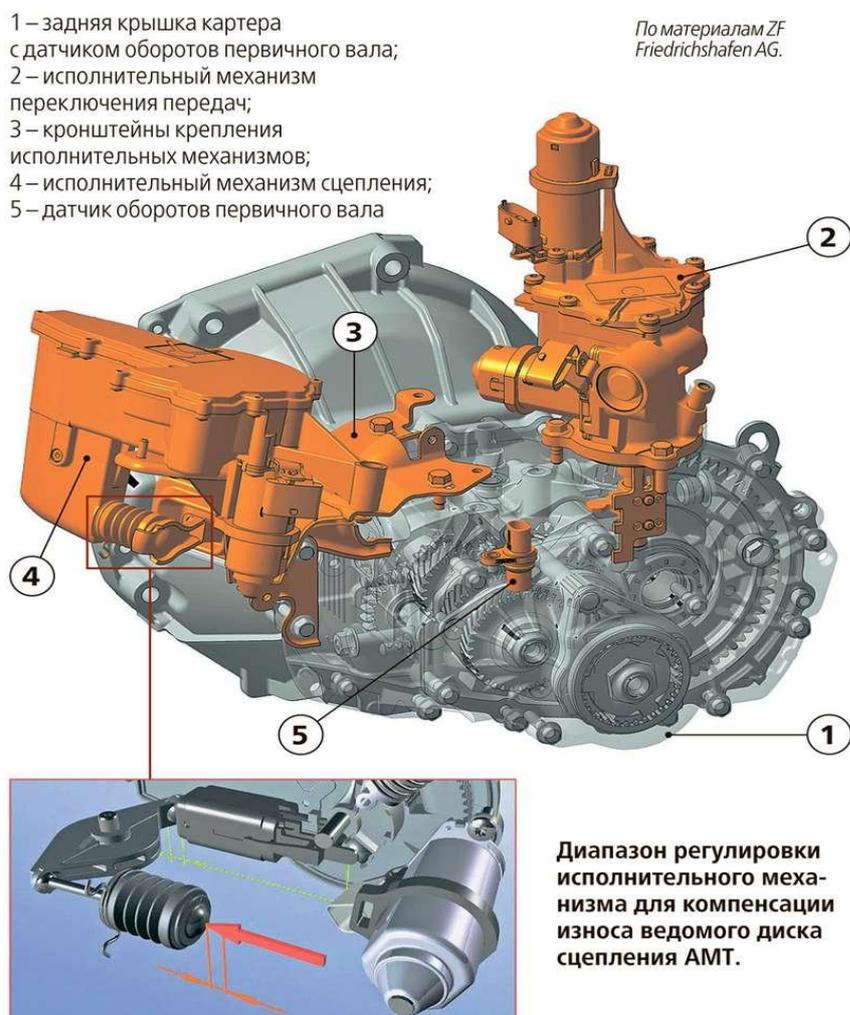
Исполнительные механизмы Роботизированной коробки переключения передач
